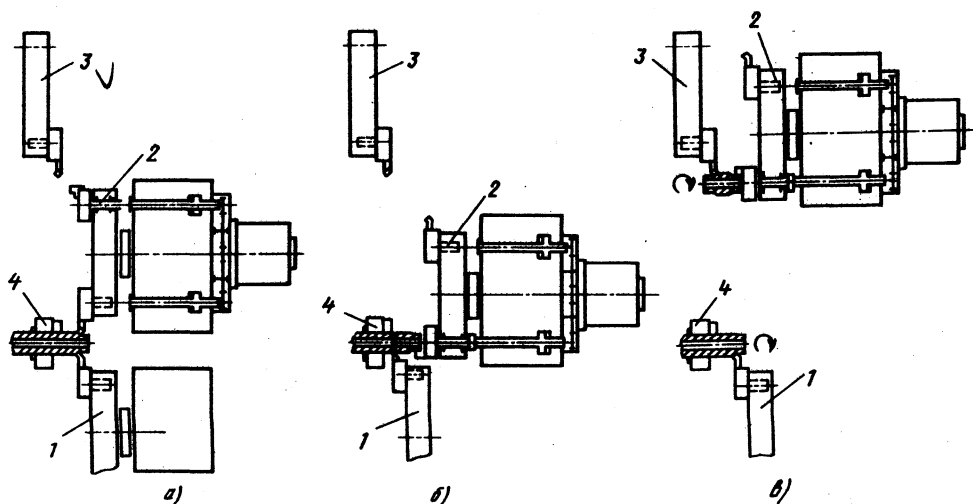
Расположение трех револьверных головок токарного станка с ЧПУ фирмы Monforts (Германия): а — обработка заготовки в шпинделе четырьмя инструментами, установленными в револьверных головках 1 и 2; б — отрезка обработанной заготовки и зажим ее в патроне револьверной головки 2; в — окончание обработки заготовки, зажатой в патроне головки 2 инструментами, расположенными в головке 3, и начало обработки следующей заготовки в шпинделе 4
